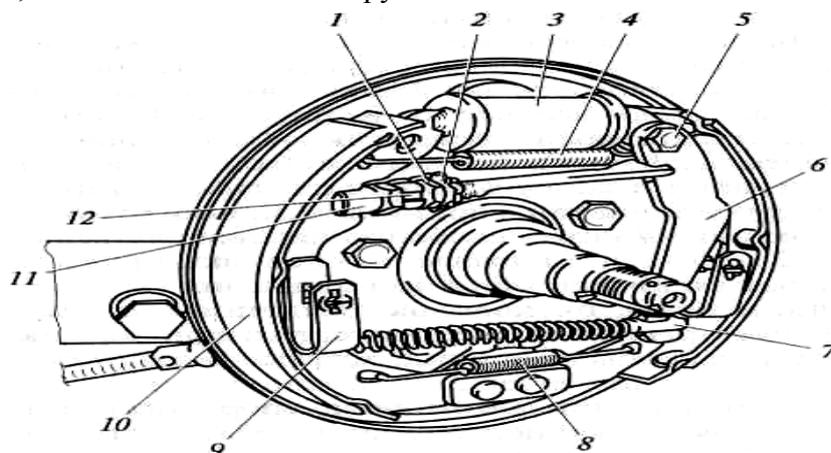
Тормозной механизм заднего колеса: 1 — гайка; 2 — храповик регулировочной гайки; 3 — колесный цилиндр; 4 — верхняя стяжная пружина колодок; 5 — палец рычага; 6 — рычаг привода; 7 — наконечник тяги; 8 — дистанционное кольцо сальника; 9 — сальник; 10 — пластинчатая пружина; 11 — тормозная колодка; 12 — толкатель.
